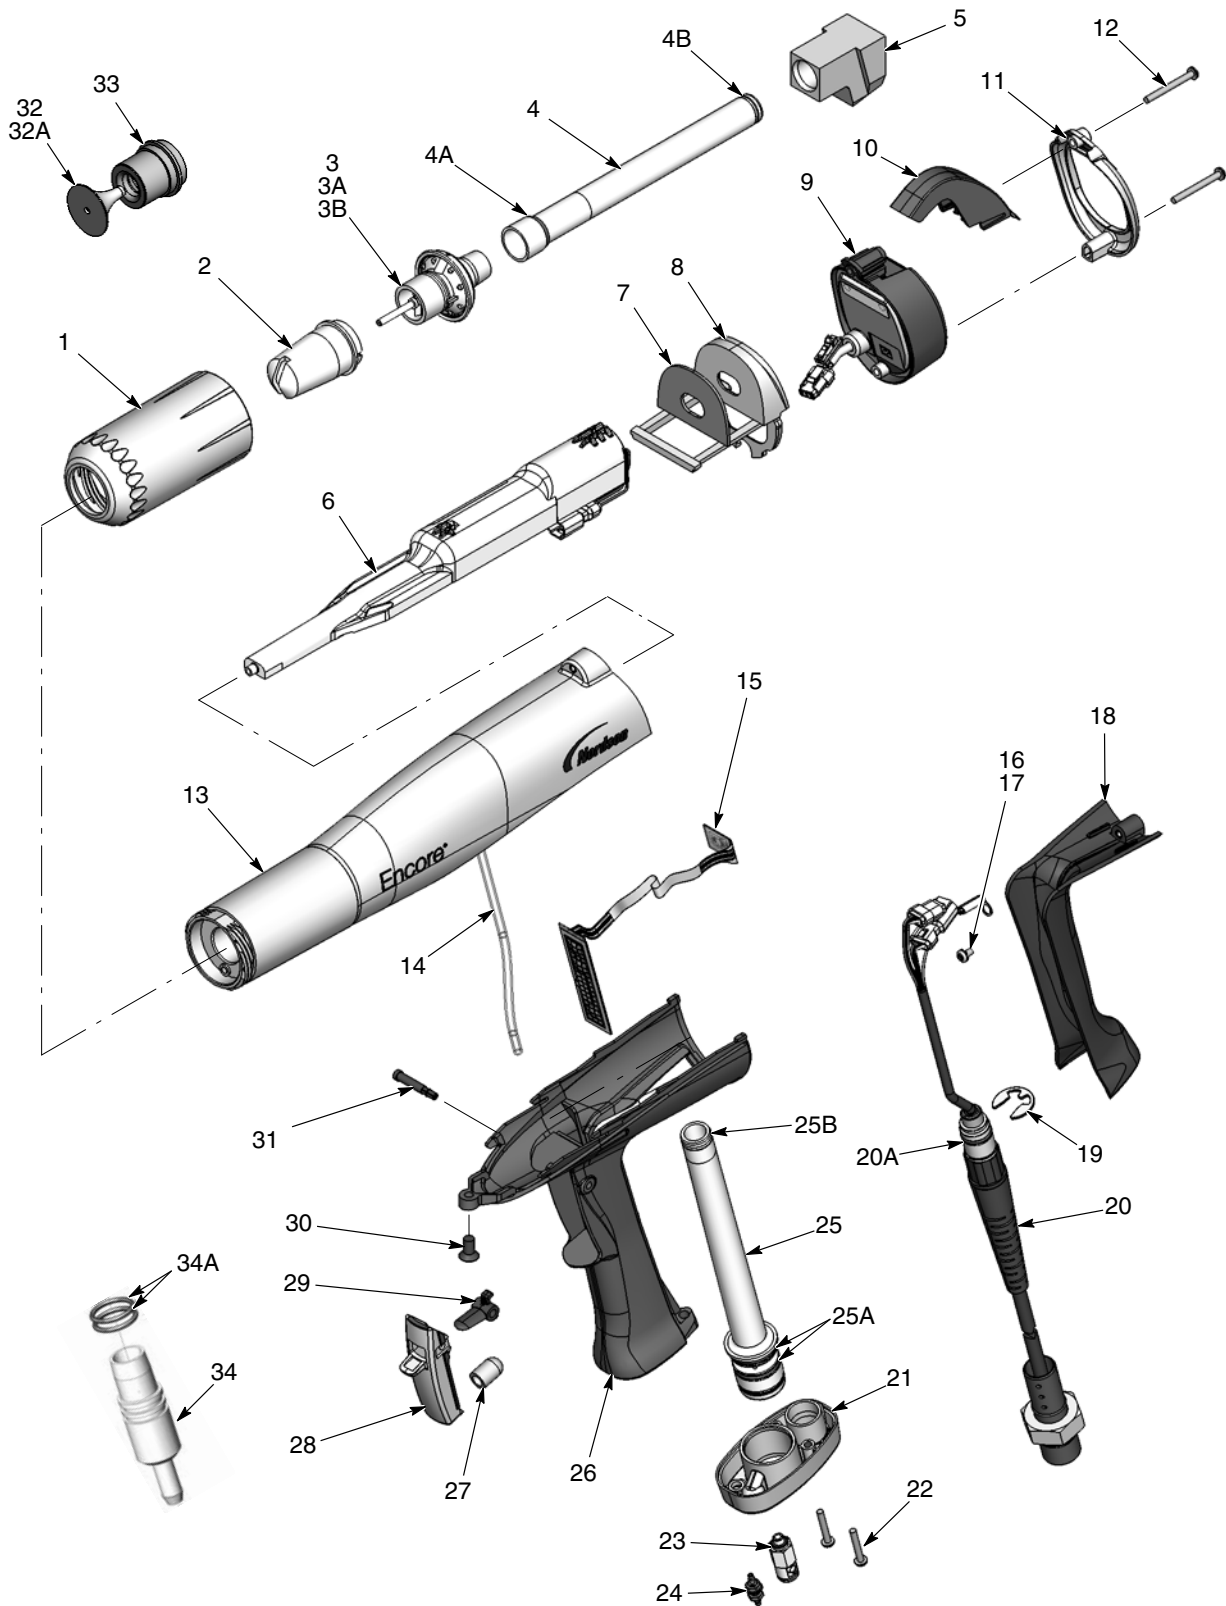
Vista explodida da pistola manual para pintura Encore XT e acessórios
